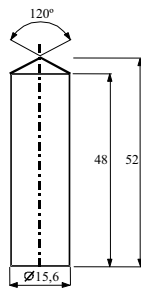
Piston cylindrique en bronze, dimensions en mm
